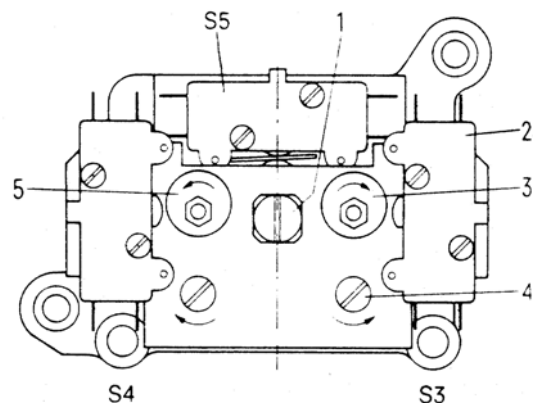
a: Rollenschaltwerk (Draufsicht)
